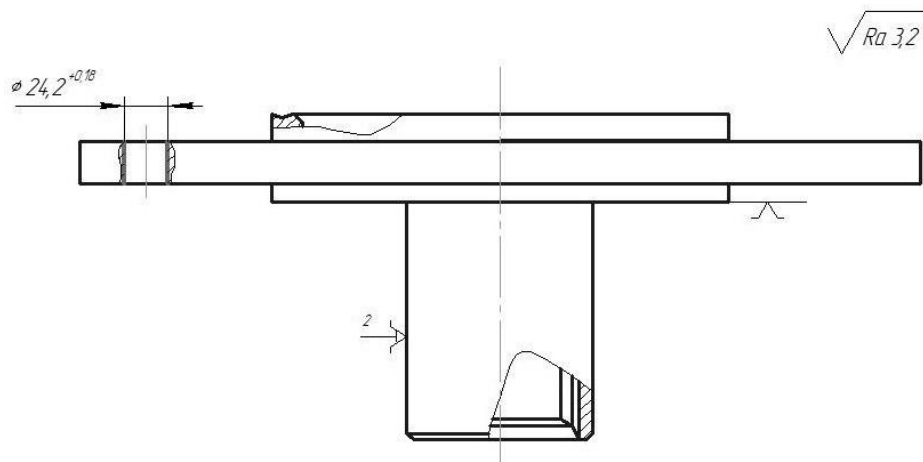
Фланець ведучої частини маточини колеса
